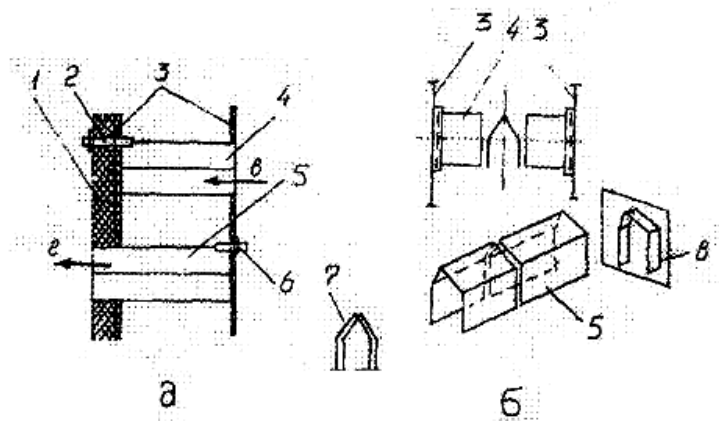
Установка коробов в шахте зерносушилки:
